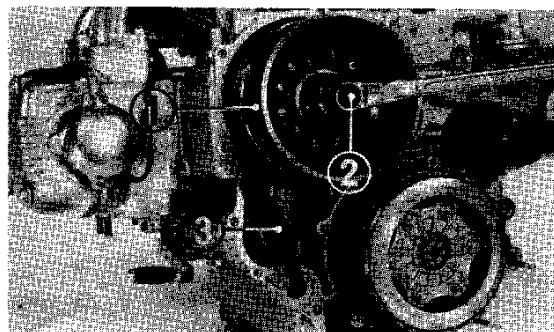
(1) Lichtmaschinen-Schwungrad
